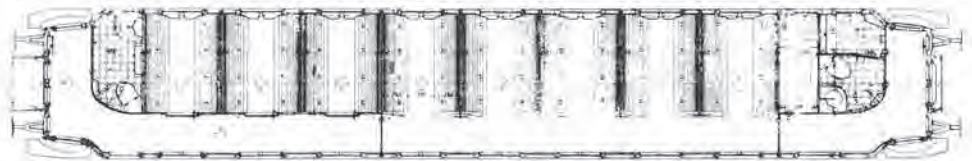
Grundriß eines preußischen Durchgangswagens 3. Klasse (1902)
